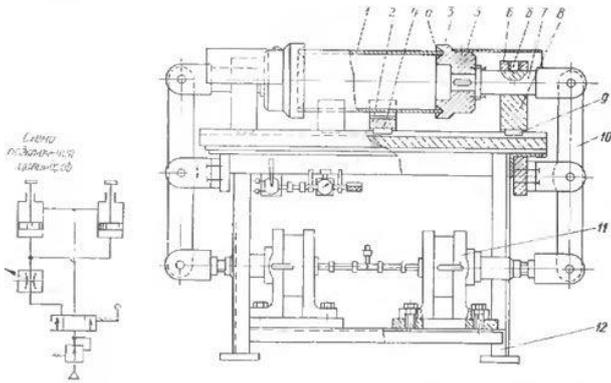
Приспособление для прихватки обечайки воздушного баллона трактора Т-150К
